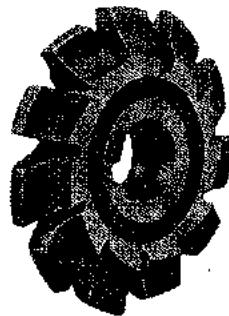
Fresa de módulo (Pratt & Whitney Co.)
